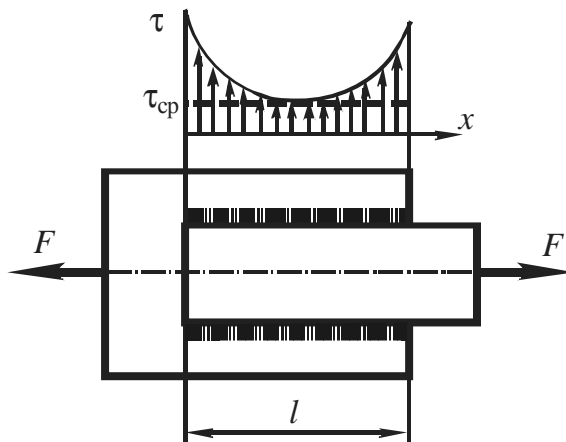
Фланговый сварной шов, нагруженный растягивающей силой
